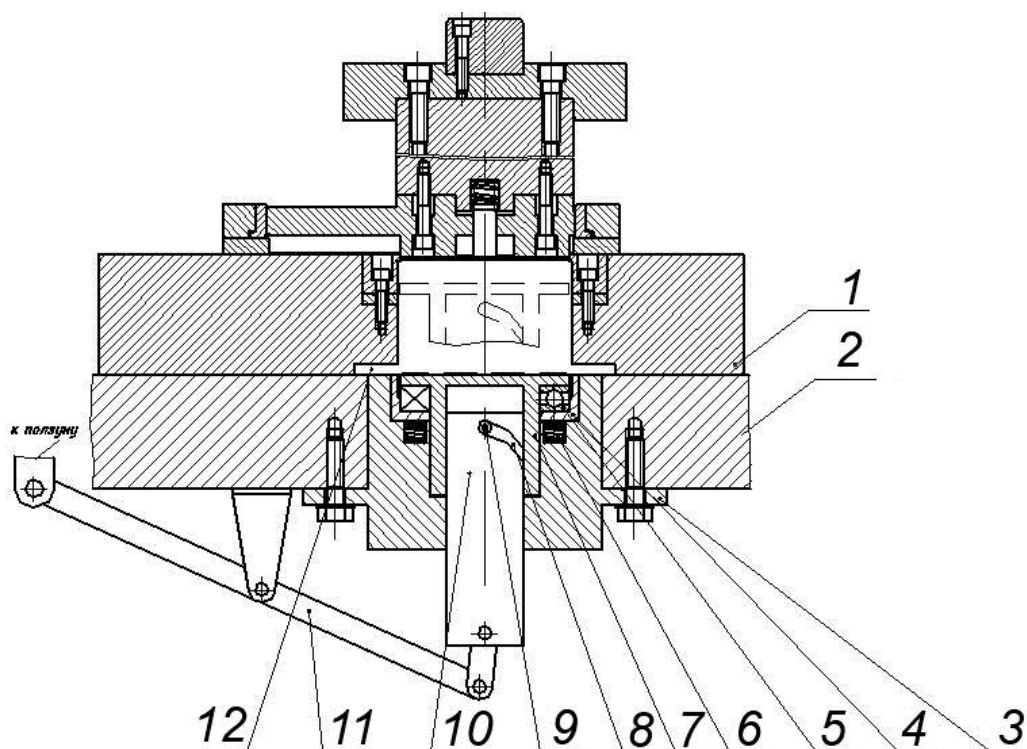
Устройство поворота вырубленной заготовки на 90° .
